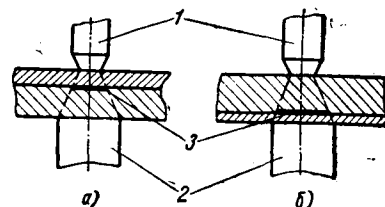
Правильное (а) и неправильное (б) положения электродов при сварке деталей из металла разной толщины: 1 — верхние электроды; 2 — опоры; 3 — площадь контакта между деталями.
